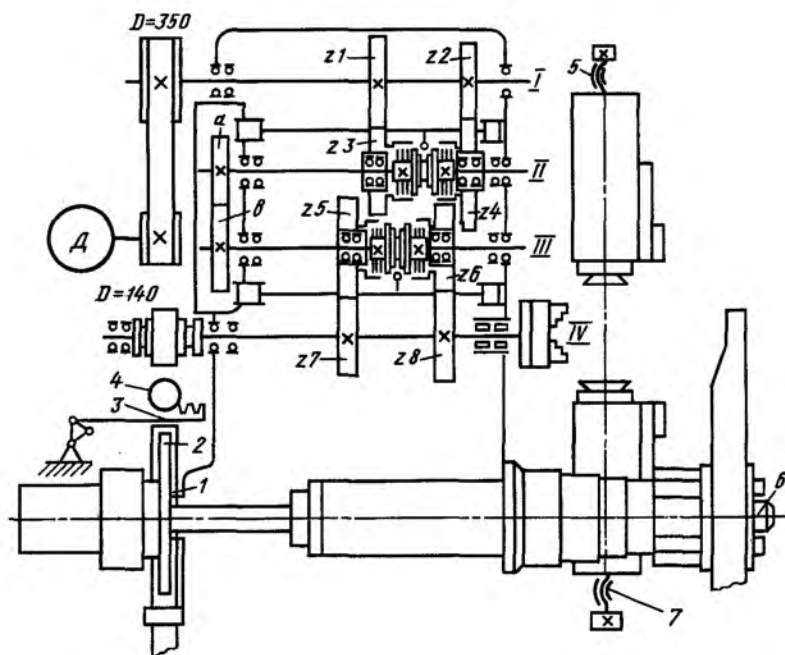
Кинематическая схема токарно-револьверного полуавтомата 1М425
